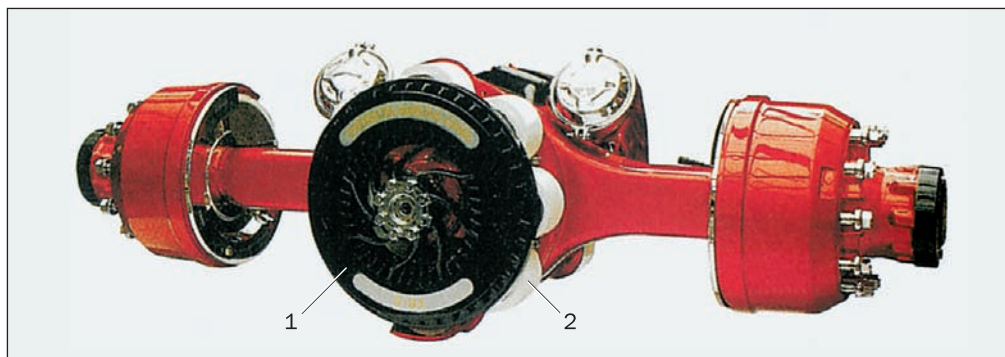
Электрический тормоз-замедлитель: 1 — ротор; 2 — обмотки статора
